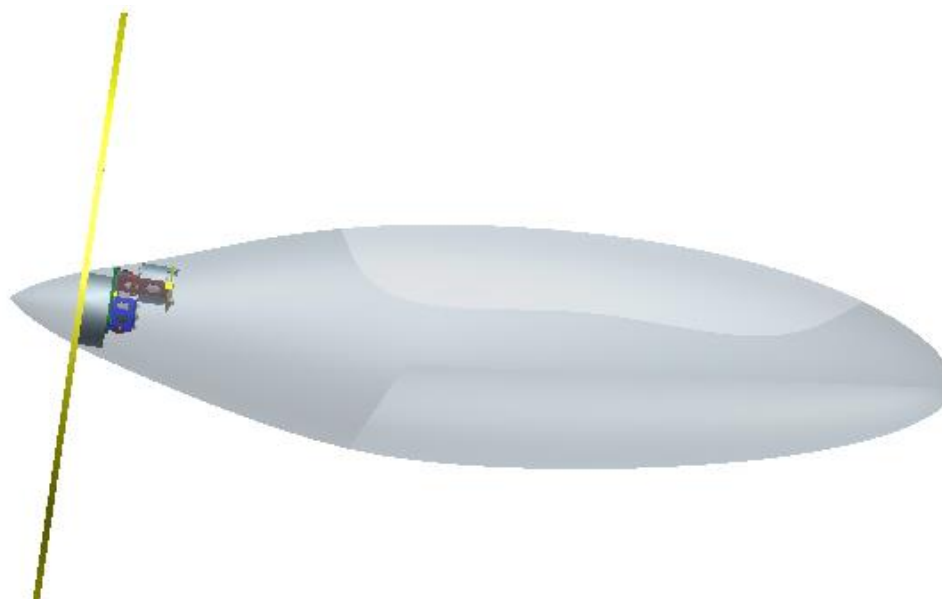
Varianta zástavby reduktoru s napínací kladkou- zdroj autor
